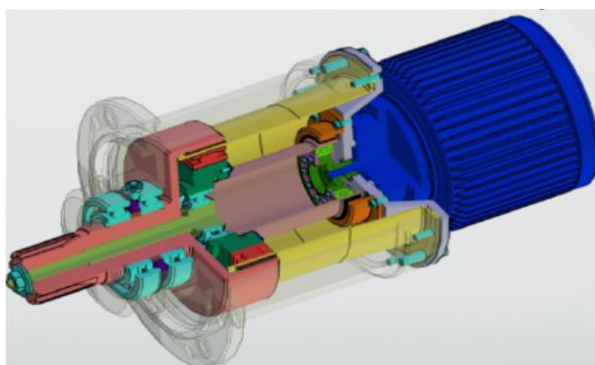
Твердотельная модель планетарно-цевочного редуктора в T-FLEX
